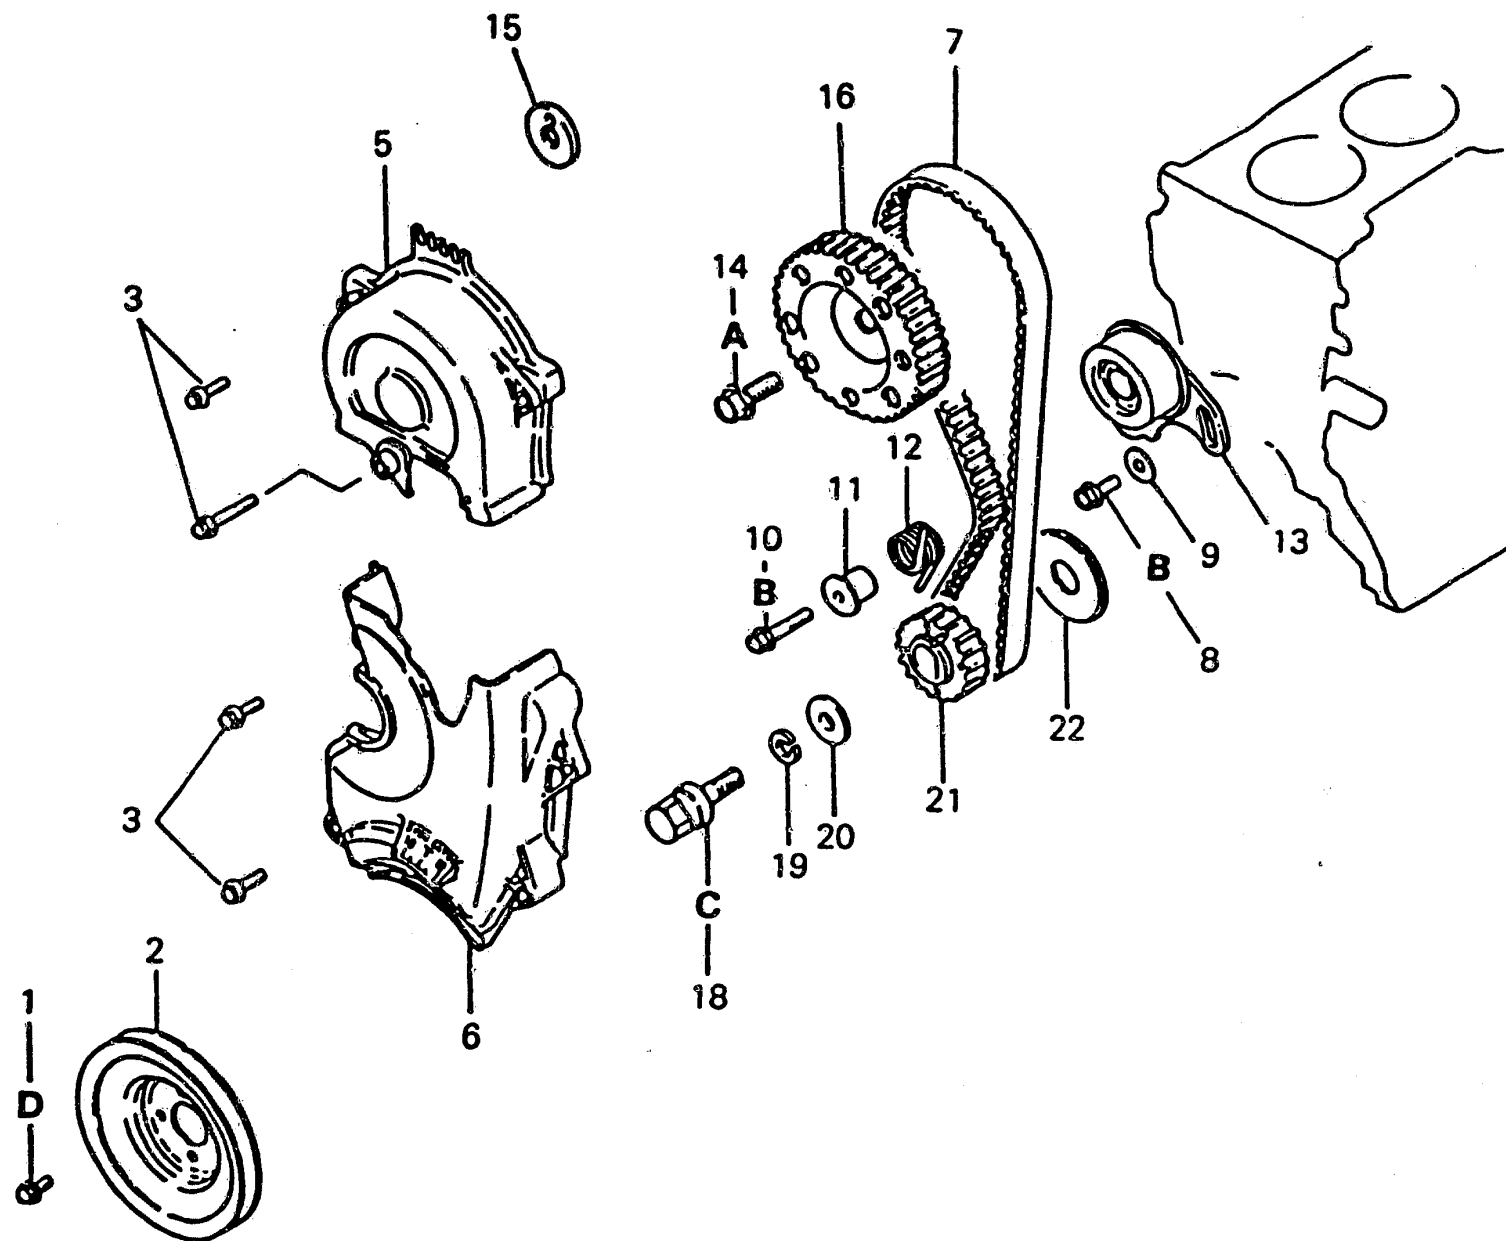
Einzelteile des Zahnriementriebs mit: 1 Flanschschraube (4) – 2 Kurbelwellen-Riemenscheibe – 3 Flanschschraube (7) – 5 Steuergehäusedeckel, oben – 6 Steuergehäusedeckel, unten – 7 Steuerriemen – 8 Flanschschraube – 9 Scheibe – 10 Flanschschraube – 11 Riemenspanner-Abstandhalter – 12 Riemen­spannfeder – 13 Riemen­spanner – 14 Flanschschraube – 15 Scheibe – 16 Nockenwellen-Zahnriemenrad – 18 Schraube für Kurbelwellen-Zahnriemenrad – 19 Federscheibe – 20 Scheibe – 21 Kurbelwellen-Zahnriemenrad – 22 Flansch. Die Zahlen geben die Demontage-Reihenfolge an.
